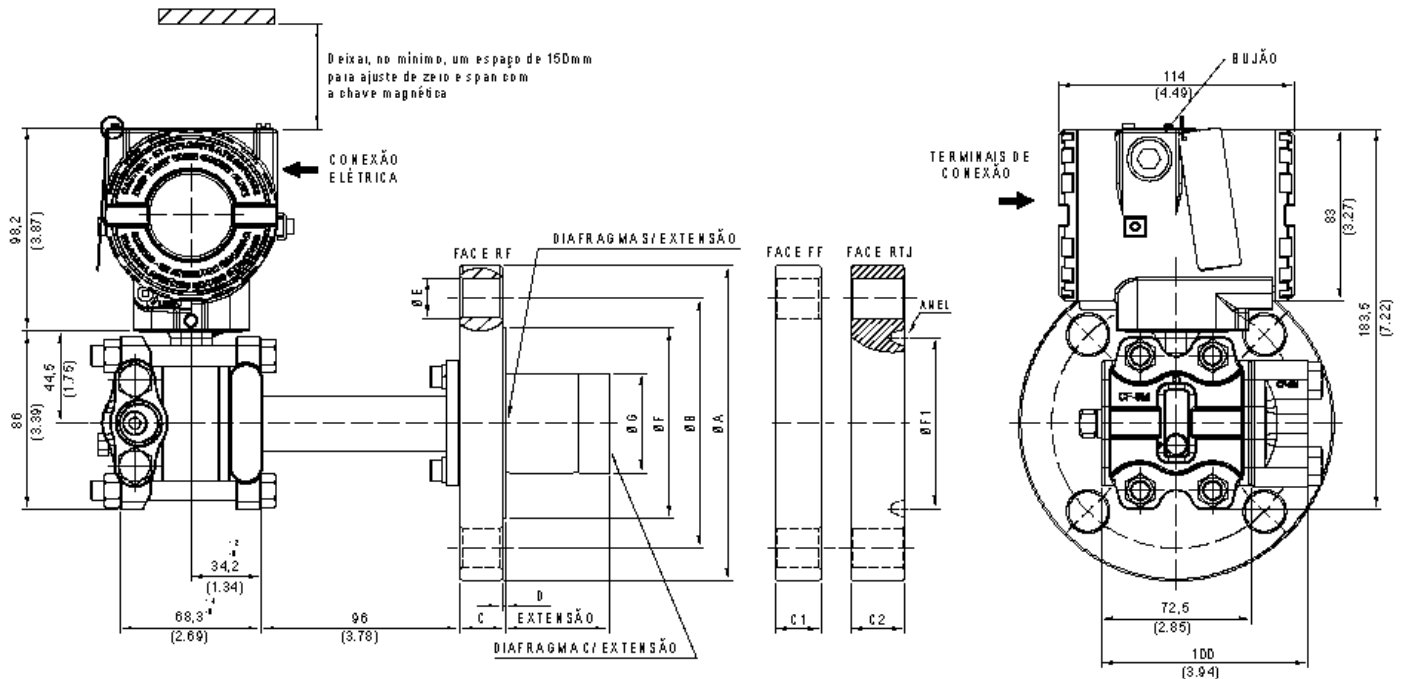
(a) - Desenho Dimensional de Montagem – Transmissor de Pressão Diferencial, Manométrica, Absoluta, Vazão, Alta Pressão Estática com Suporte
